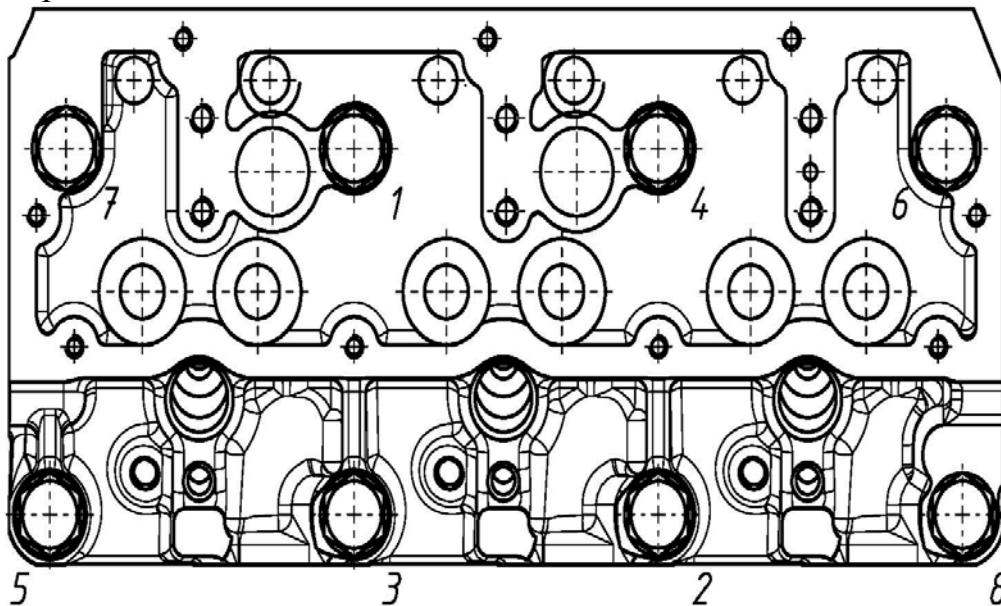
Схема последовательности затяжки болтов крепления головки цилиндров.
